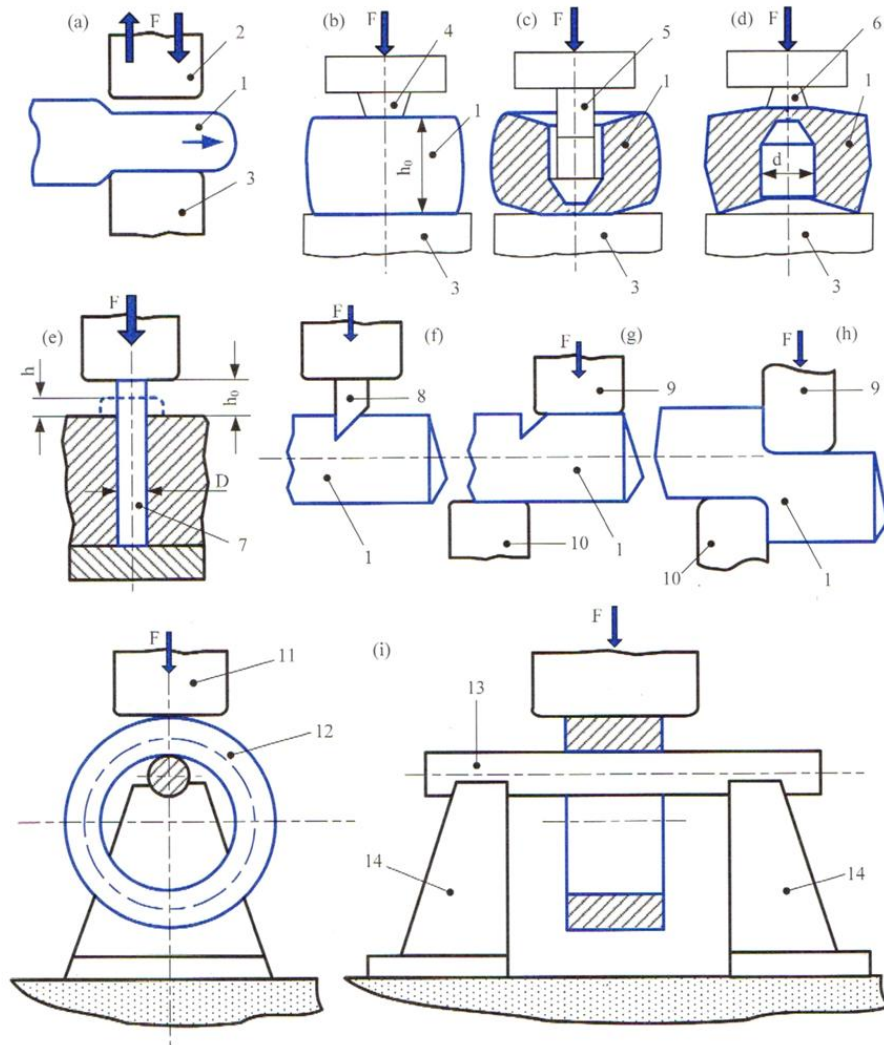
Opération préalable ou (1 = lingotière; 2 = couperet; 3 = brut; 4 = guillotine qui fait une coupe définitive du brut; 5 = lopin préparé; d, D, L = dimensions; F = force) [3].
